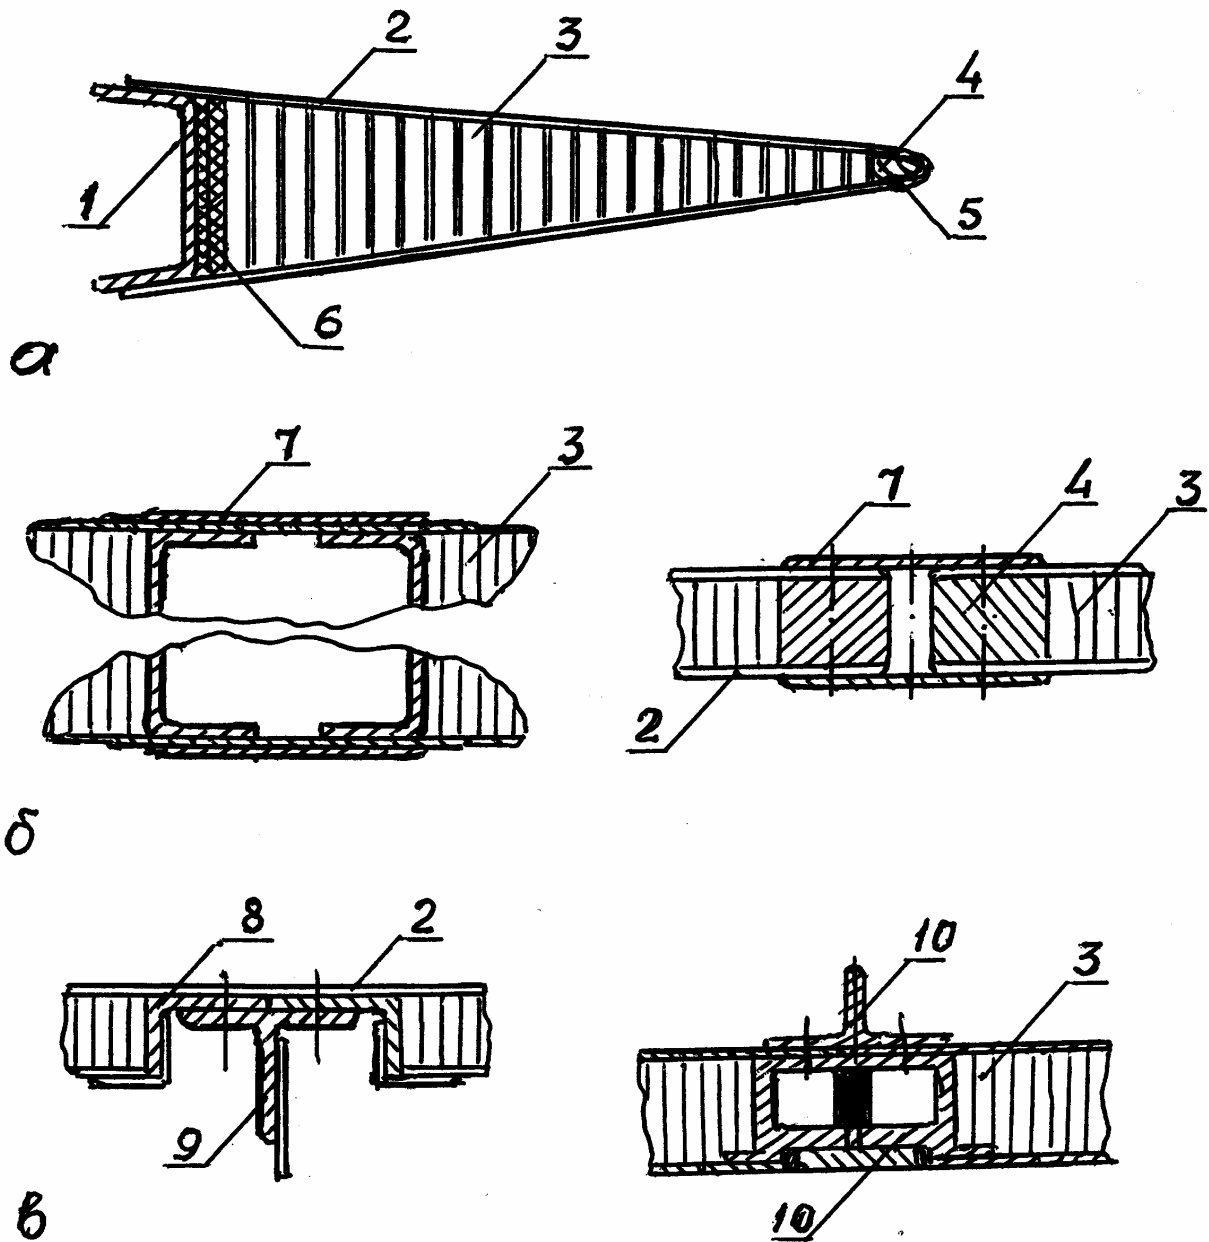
Конструктивные схемы и способы соединений в конструкциях с сотовым наполнителем: а – соединение обшивок с сотовым наполнителем и элементами каркаса; б – соединение сотовых конструкций между собой; в – соединение сотовых панелей между собой через элементы каркаса. 1 – каркас; 2 – обшивка; 3 – сотовый наполнитель; 4 – вкладыш; 5 – законцовочный профиль, выполненный перегибом обшивки; 6 – вспенивающаяся композиция; 7 – накладка; 8 – профиль стыковочный панели; 9 – профиль каркаса; 10 – профиль специальный
